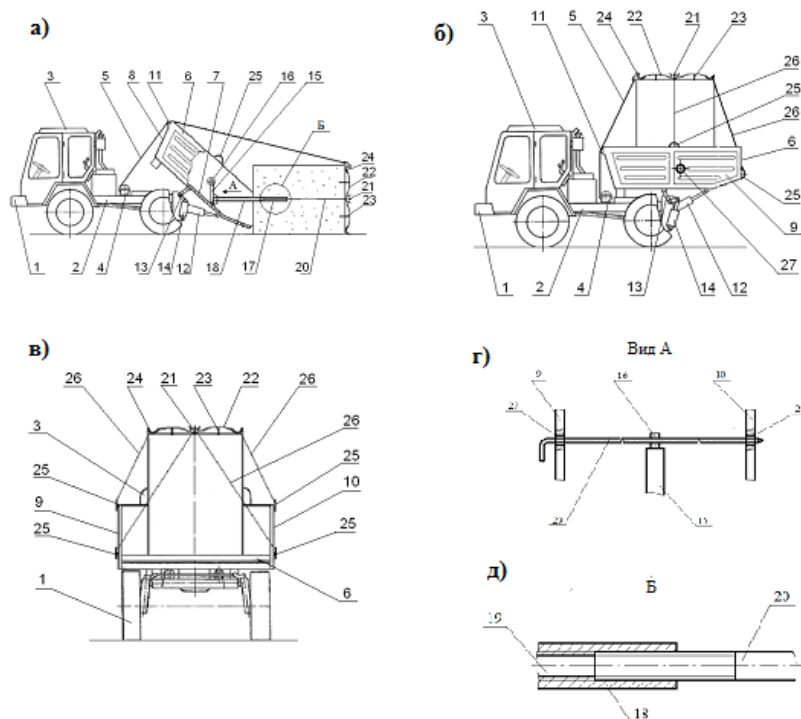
Экологичный сеноуборочный агрегат на базе автотрактора: а – вид сбоку на агрегат в погрузочном положении при опущенном самосвальном кузове; б – вид сбоку на агрегат с самосвальным кузовом в транспортном положении; в – вид сзади на сеноуборочный агрегат; г – вид А; д – выносной элемент Б
